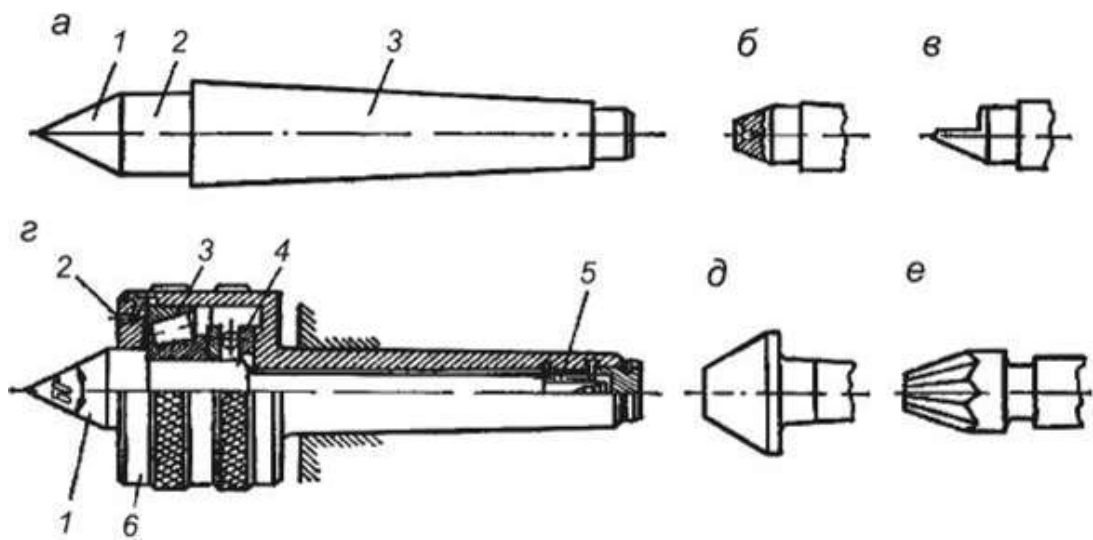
Токарні центри для підтримки вільного кінця заготовки:
